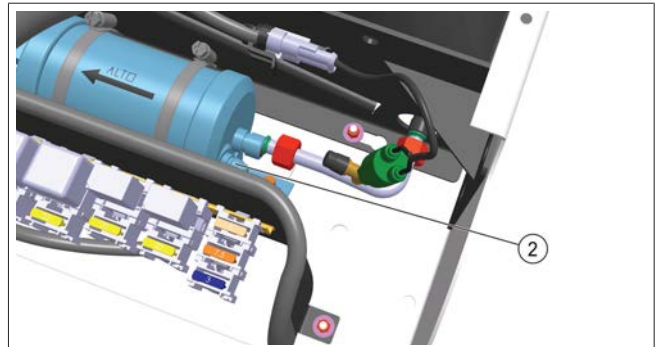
Punto di carica Frigo Top, lato alta pressione
